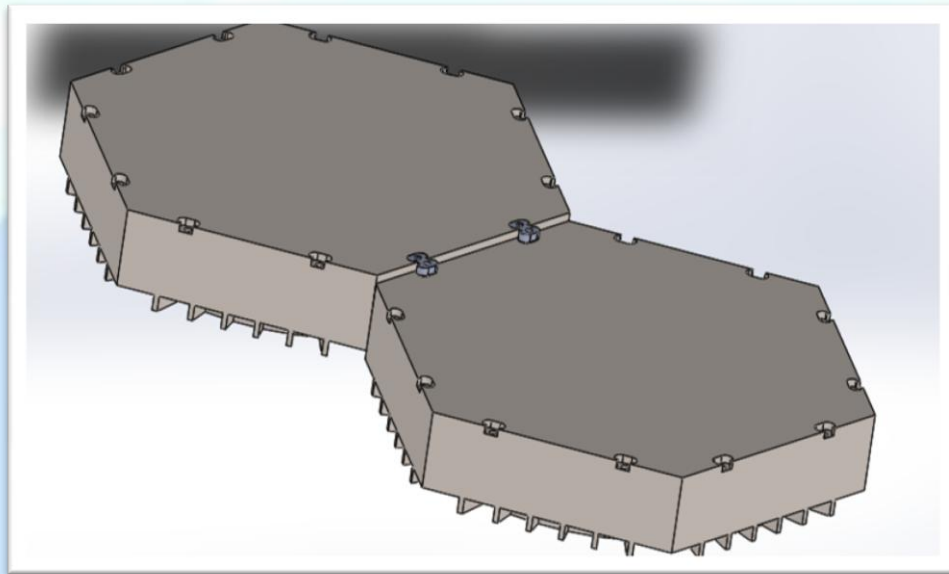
Ensamblaje permitiendo el desplazamiento vertical
